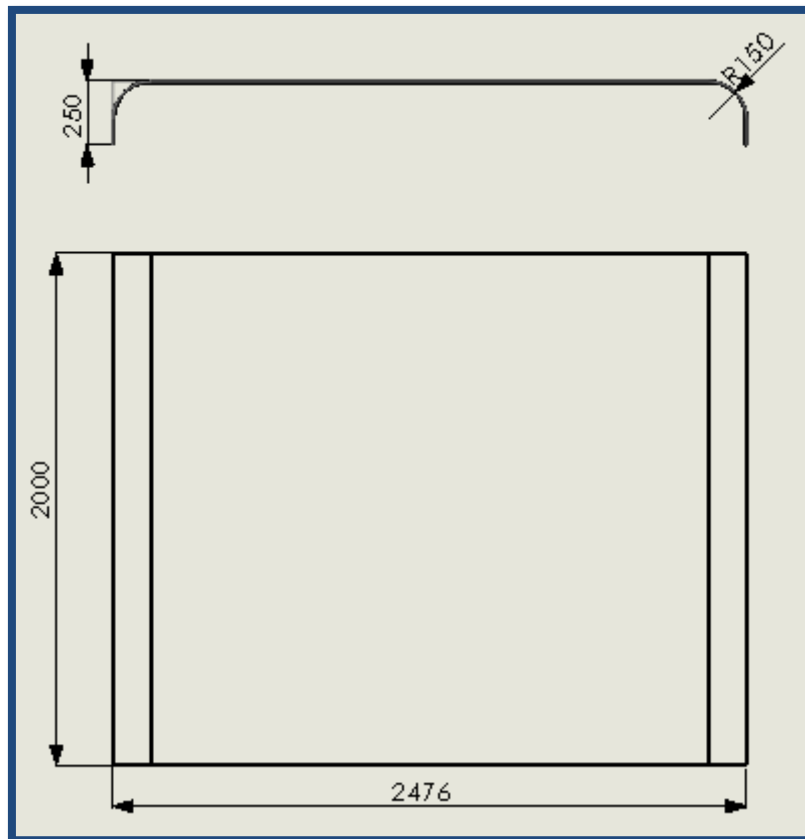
Dimensiones generales de la chapa trasera.
